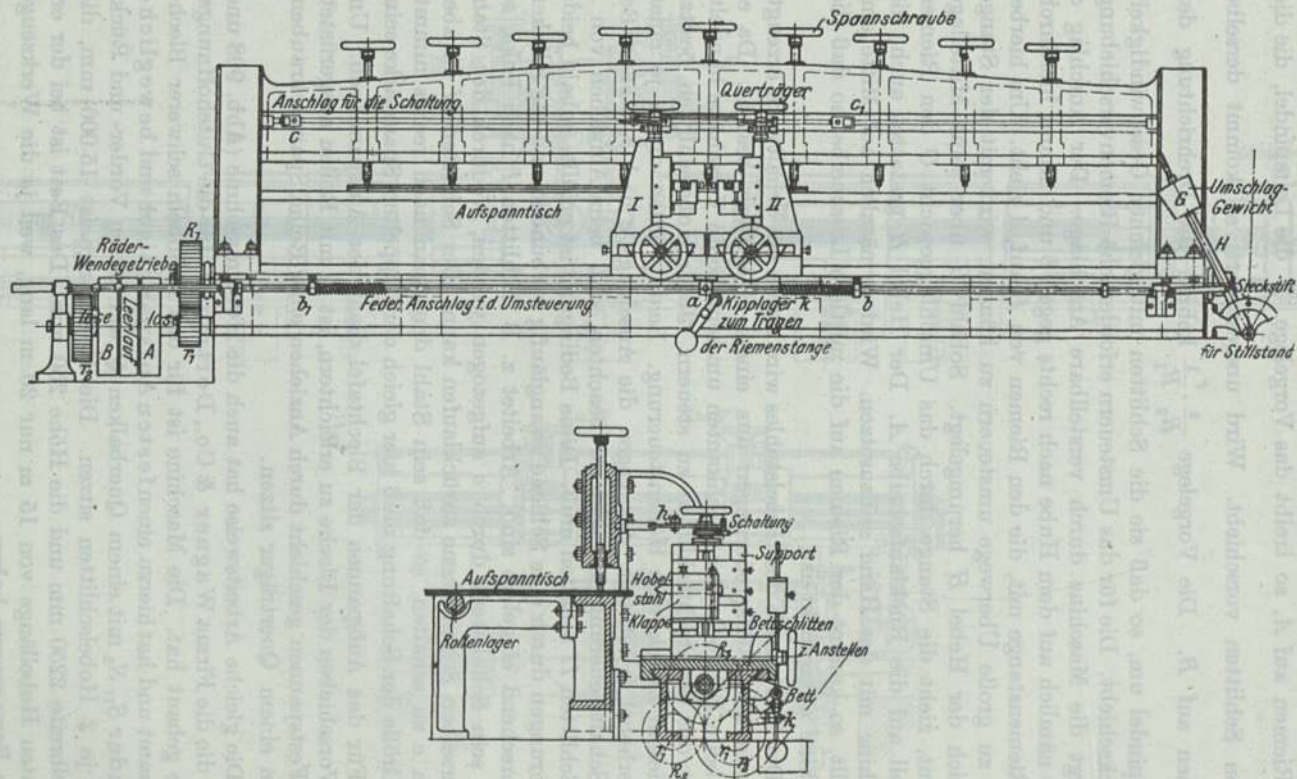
und 907. Blechkantenhobmaschine. Kalker Maschinenfabrik, Kalk bei Köln a. Rh.
